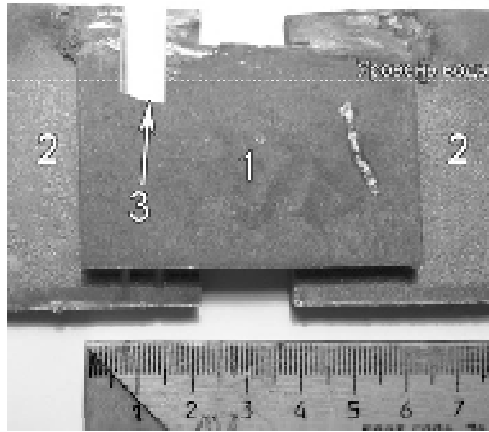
Сварные соединения закаленной стали 120Г3С2 (1) и стали 09Г2С (2), 3 – место отбора образца для исследования структуры ЗТВ
